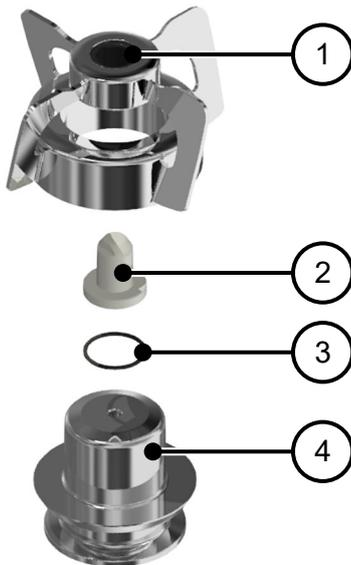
Baugruppe mit Gleitlager, Explosionsdarstellung
